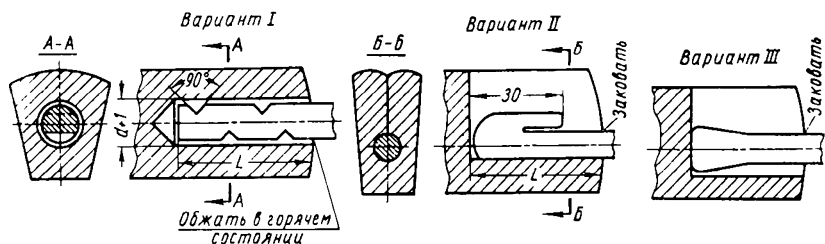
Способы крепления и заделки вставных рукояток для инструмента
